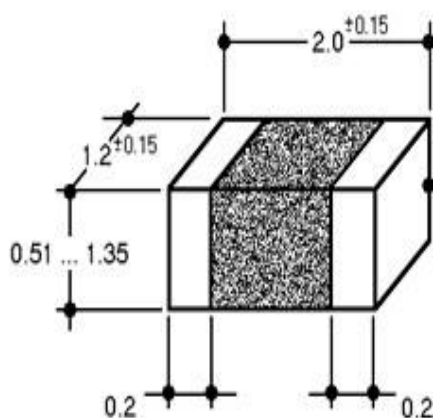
Габаритні розміри керамічного конденсатора
